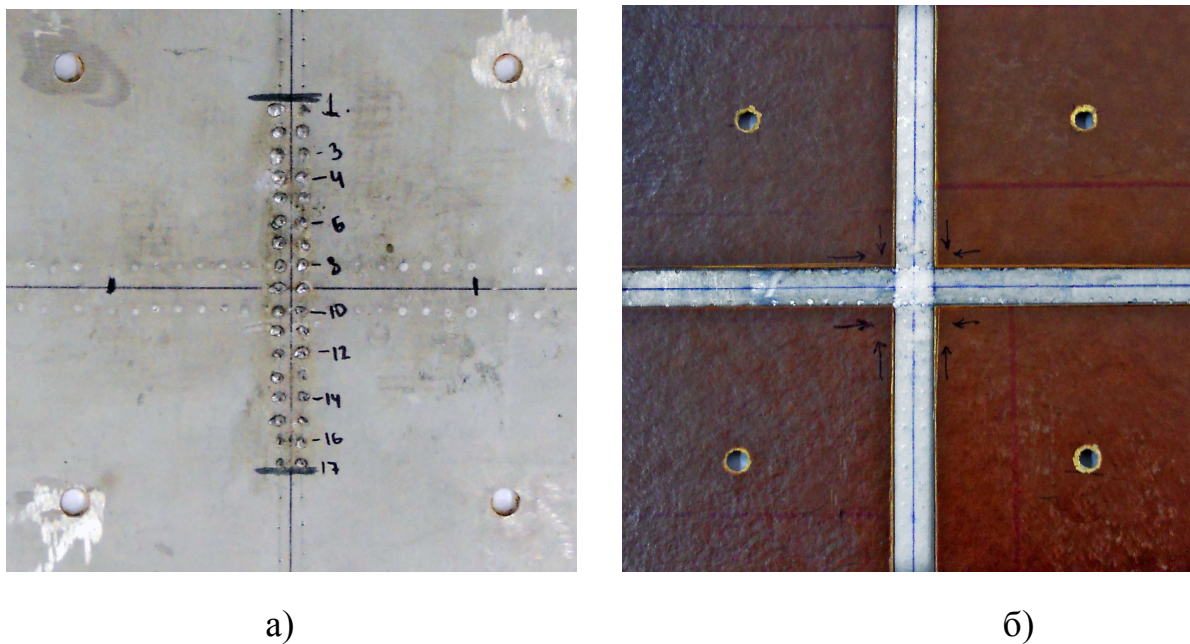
Экспериментальный образец: а) листовая заготовка со стороны выводов; б) листовая заготовка со стороны противоположной выводам
